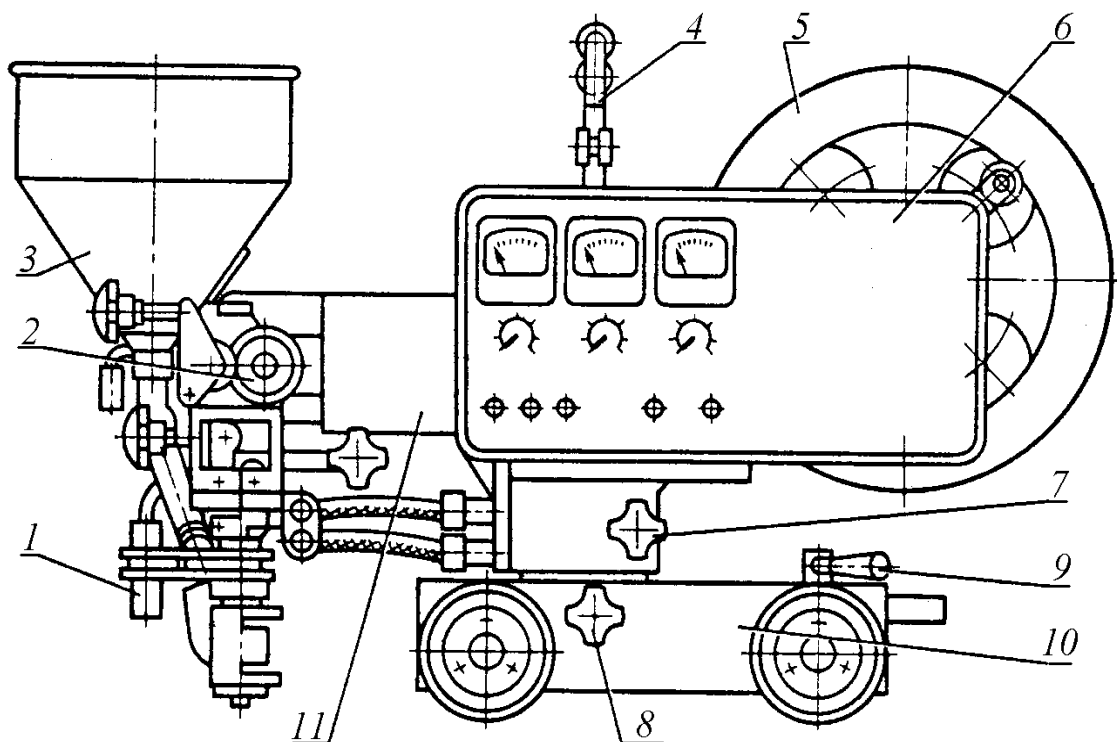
Сварочный автомат тракторного типа АДФ: 1 – светуказатель; 2 – подающий механизм; 3 – флюсобункер; 4 – промежуточные ролики подачи сварочной проволоки; 5 – кассета с электродной проволокой; 6 – пульт управления; 7, 8 – маховики регулировки положения сварочной головки относительно сварного шва; 9 – рукоятка для зацепления с приводом самоходной тележки; 10 – самоходная тележка; 11 – сварочная головка
